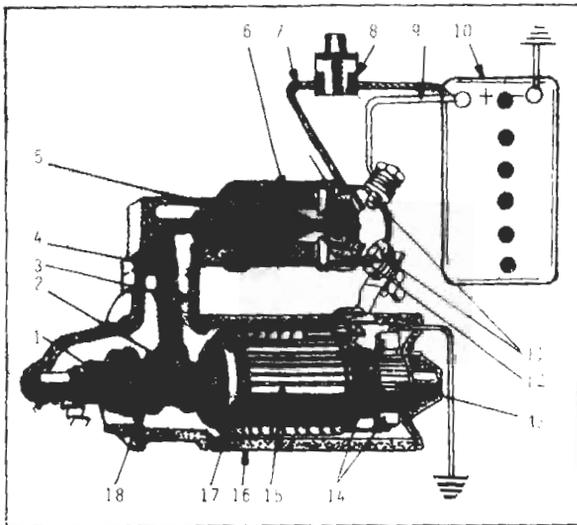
Sección de un motor de arranque. 1.- Piñón. 2.- Horquilla. 3.- Eje basculamiento de la palanca. 4.- Palanca pesada se utilizaba un motor auxiliar de gaso- 5.- Núcleo del relé. 6.- Embobinado del relé. 7.- Cable del interruptor de arranque al relé. 8.- Interruptor de arranque. 9.- Cable grueso de la batería. 10.- Batería. 11.- Contactos del relé. 12.- Placa del relé. 13.- Colector. 14.- Escobillas. 15.- Inducido. 16.- Armadura. 17.- Bobinas inductoras. 18.- Collar.
